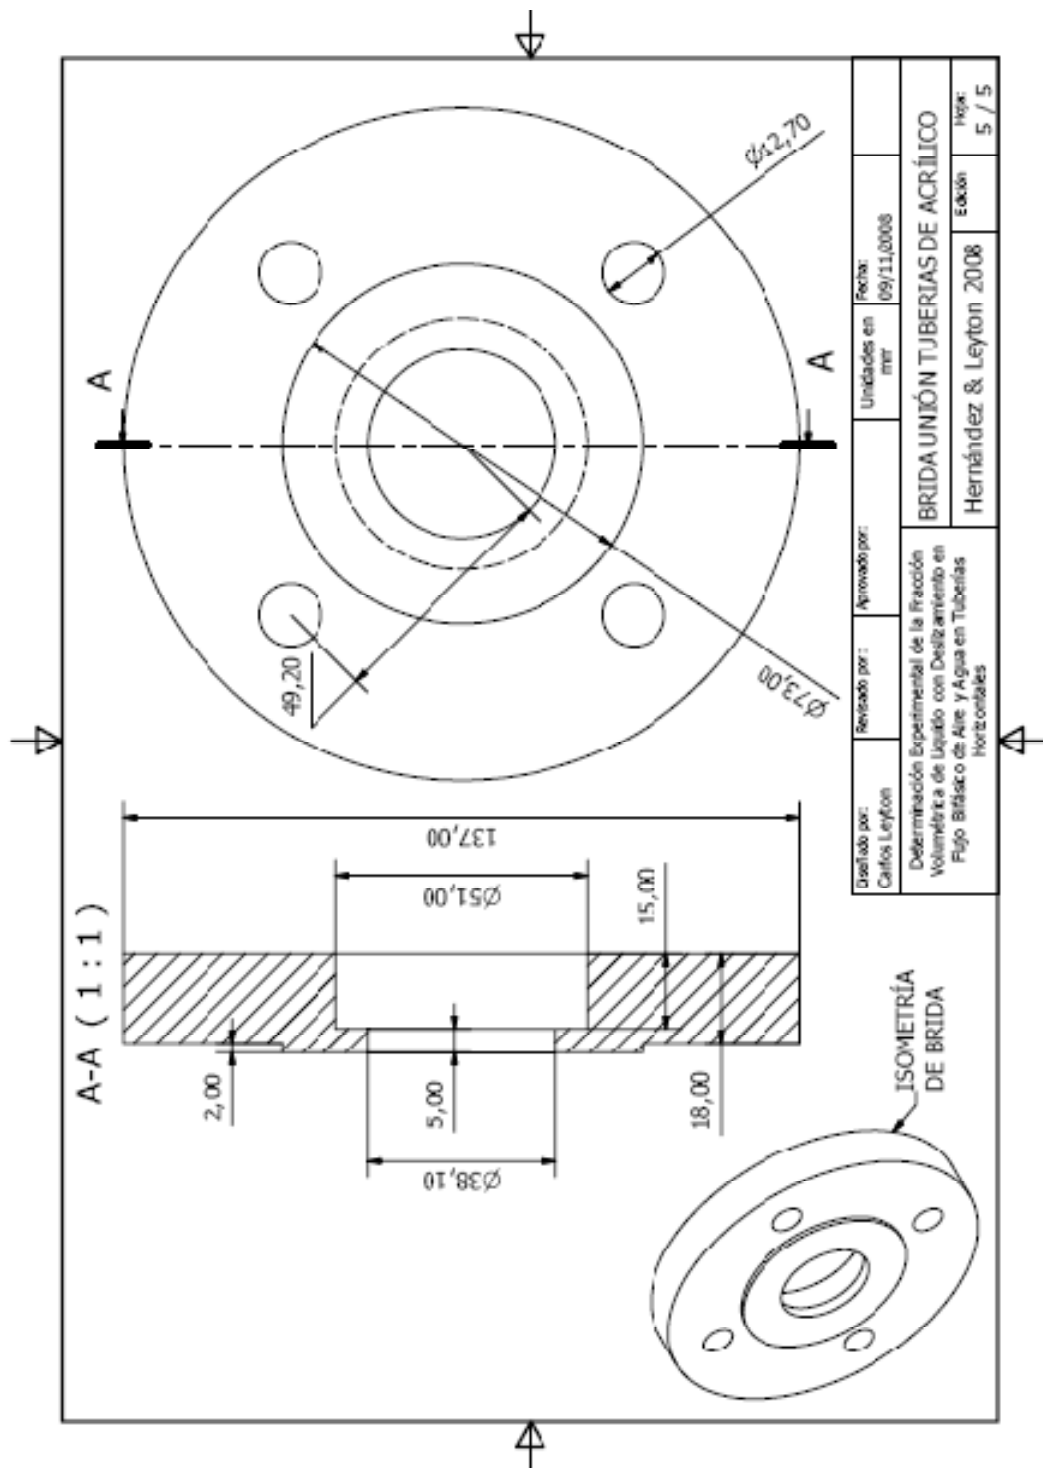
Planos constructivos de la Sección de desvío de flujo (5/5).
